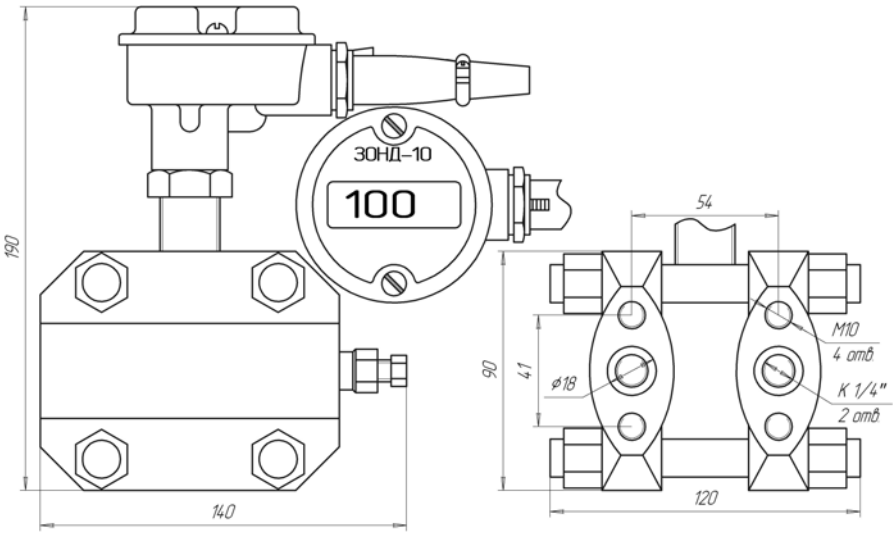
Модель 1172. ЖКИ индикатор, разъем с фиксатором.
